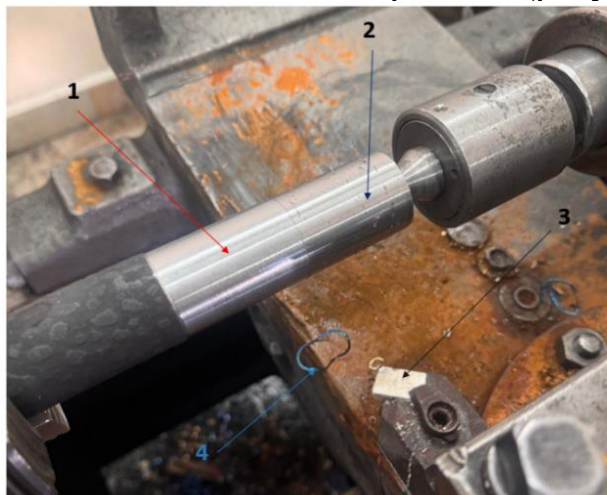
Внешний вид минералокерамической режущей пластины и поверхности детали после механической чистовой обработки.
